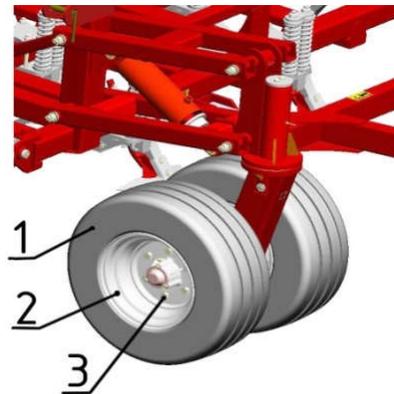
Опорно-транспортні колеса центральної рами культиваторної частини:
